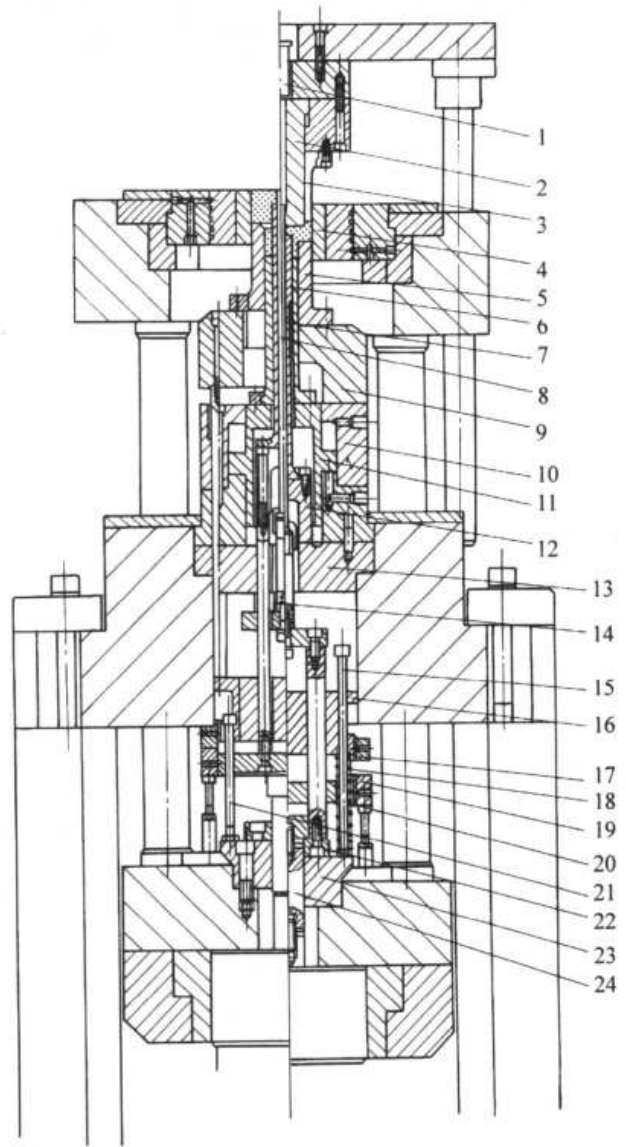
带内外台阶 V 型零件压坯成形模具
